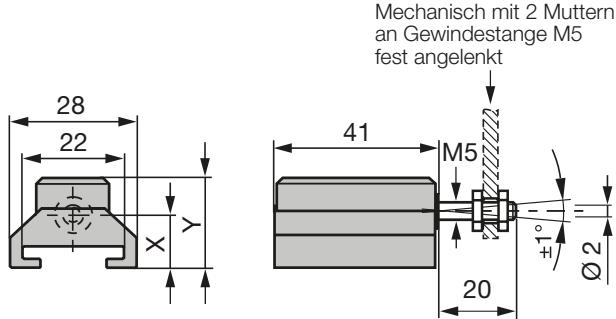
Einbaumaße Positionsgeber BTL5-M/N-2814-1S
